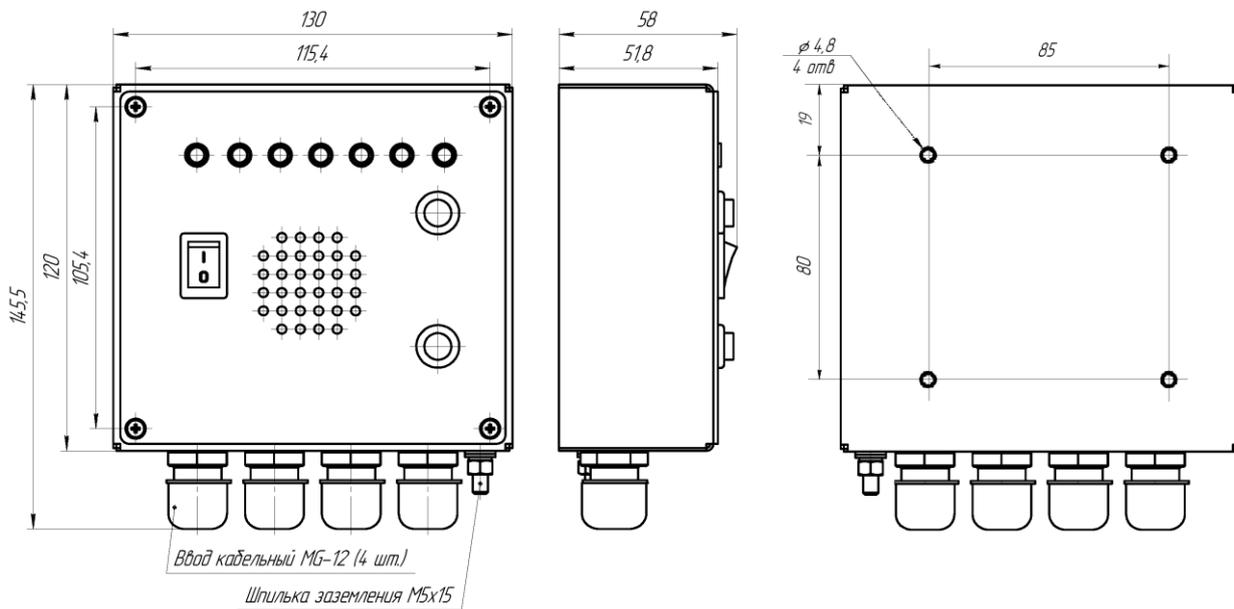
Габаритные и установочные размеры БС-206
